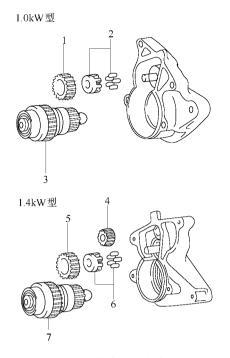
安装齿轮和离合器部件 1、5—中间齿轮 2、6—轴承 3、7—离合器部件 4—小齿轮
